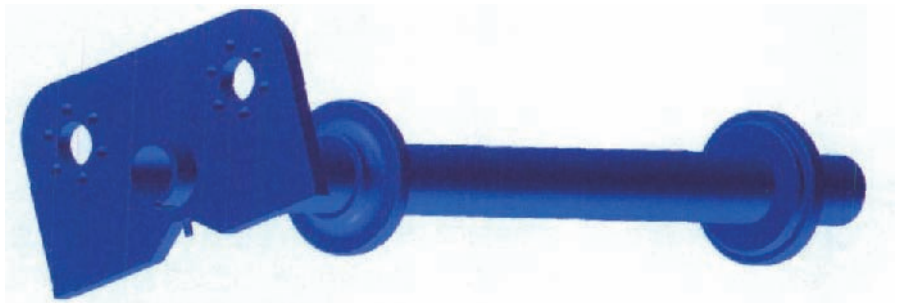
补燃室壳体和进气道焊缝的焊接夹具主要零件示意图
